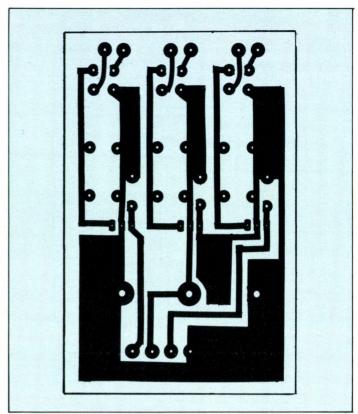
Circuit imprimé de l'alimentation vu côté soudures.
